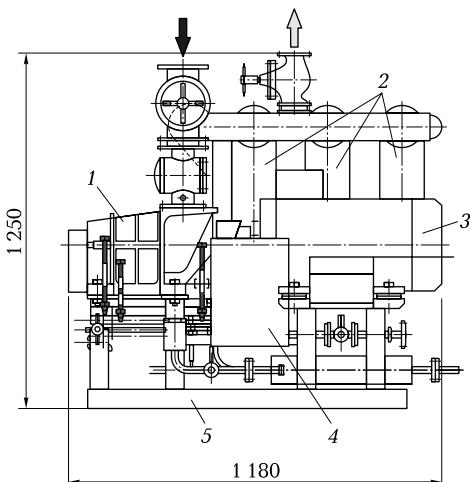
Общий вид аммиачного компрессорного агрегата 2А50Б-7:
